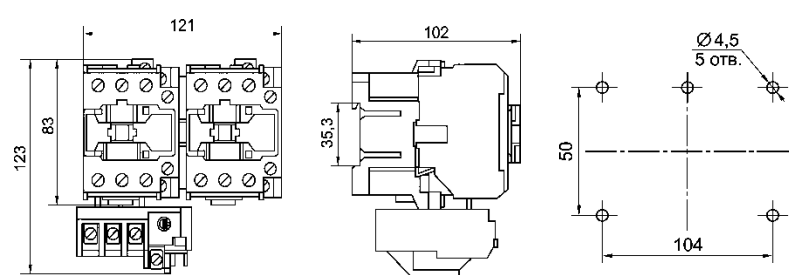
Пускатель реверсивный ПМ12-040 40А.
